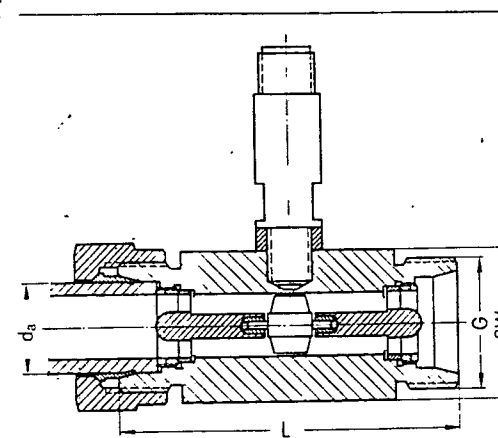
/6 Turbinen-Mengenmeßgerät mit Rohrverschraubung, Maße
